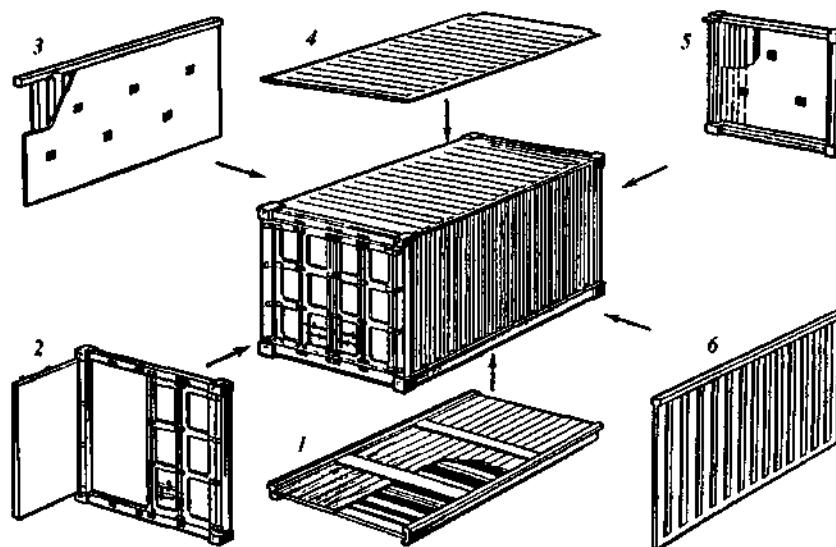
Общий вид крупнотоннажного контейнера и основные элементы его конструкции: 1 — нижняя рама с полом; 2 — дверная рама с двустворчатой дверью; 3 — боковая стена с внутренней обшивкой; 4 — крыша; 5 — торцевая стена; 6 — боковая стена без внутренней обшивки
